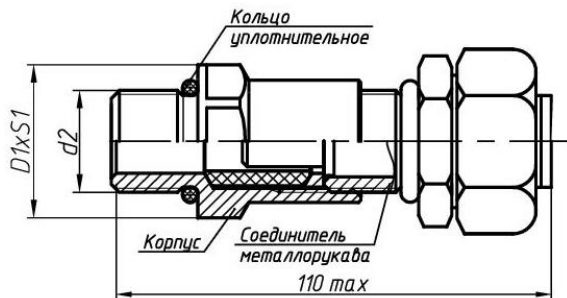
ExdKBU-M с соединителем металлоруква Герда-СГ с наружной резьбой. Размеры см в таблице А.8
